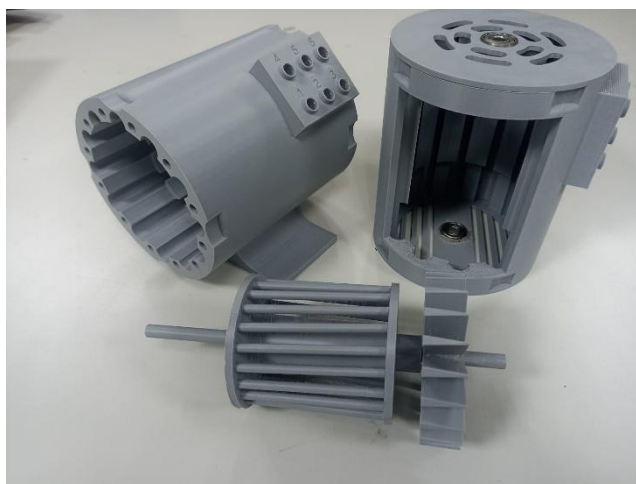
Rotor do motor de (CA) modelado em 3D pelo Fusion 360.
